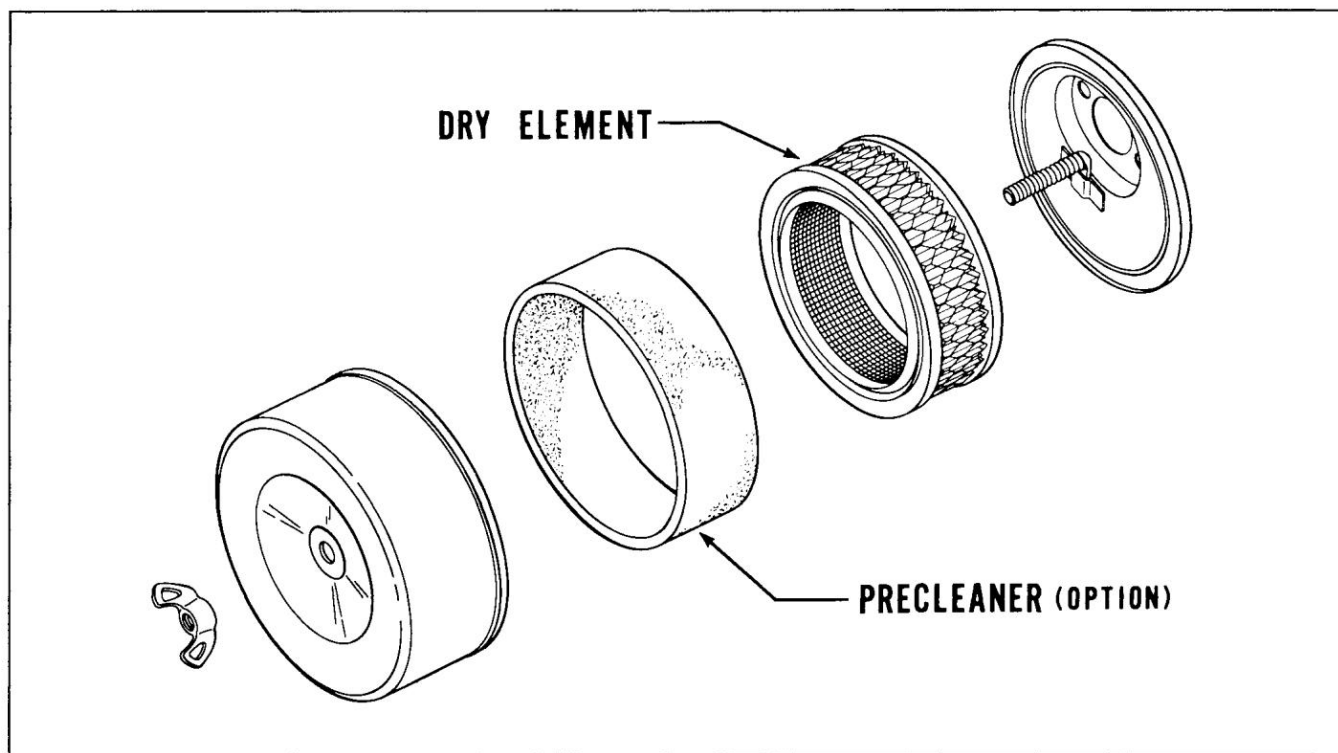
Ensemble de filtre à air - Vue éclatée.
